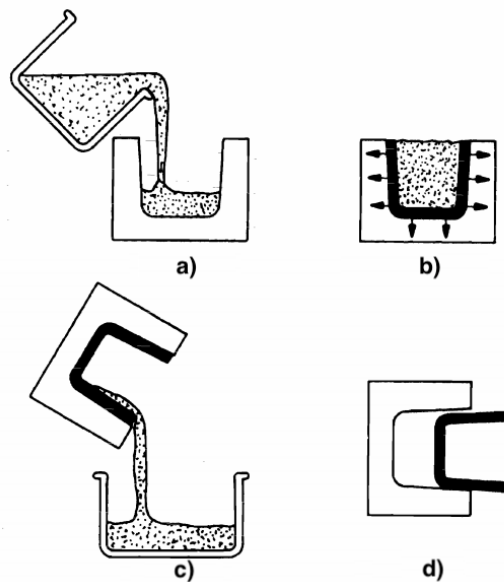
Esquema del proceso de *slip casting*: a) llenado del molde. b) molde completamente lleno. c) vaciado del contenido. d) retiro del molde.
